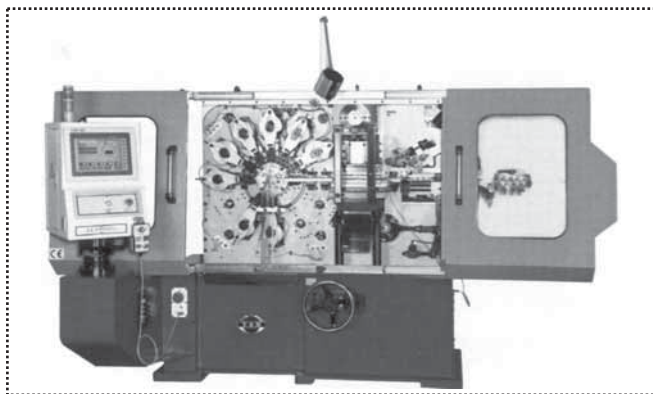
Станок мод. YSM-36Т для формовки проволоки и металлической ленты
